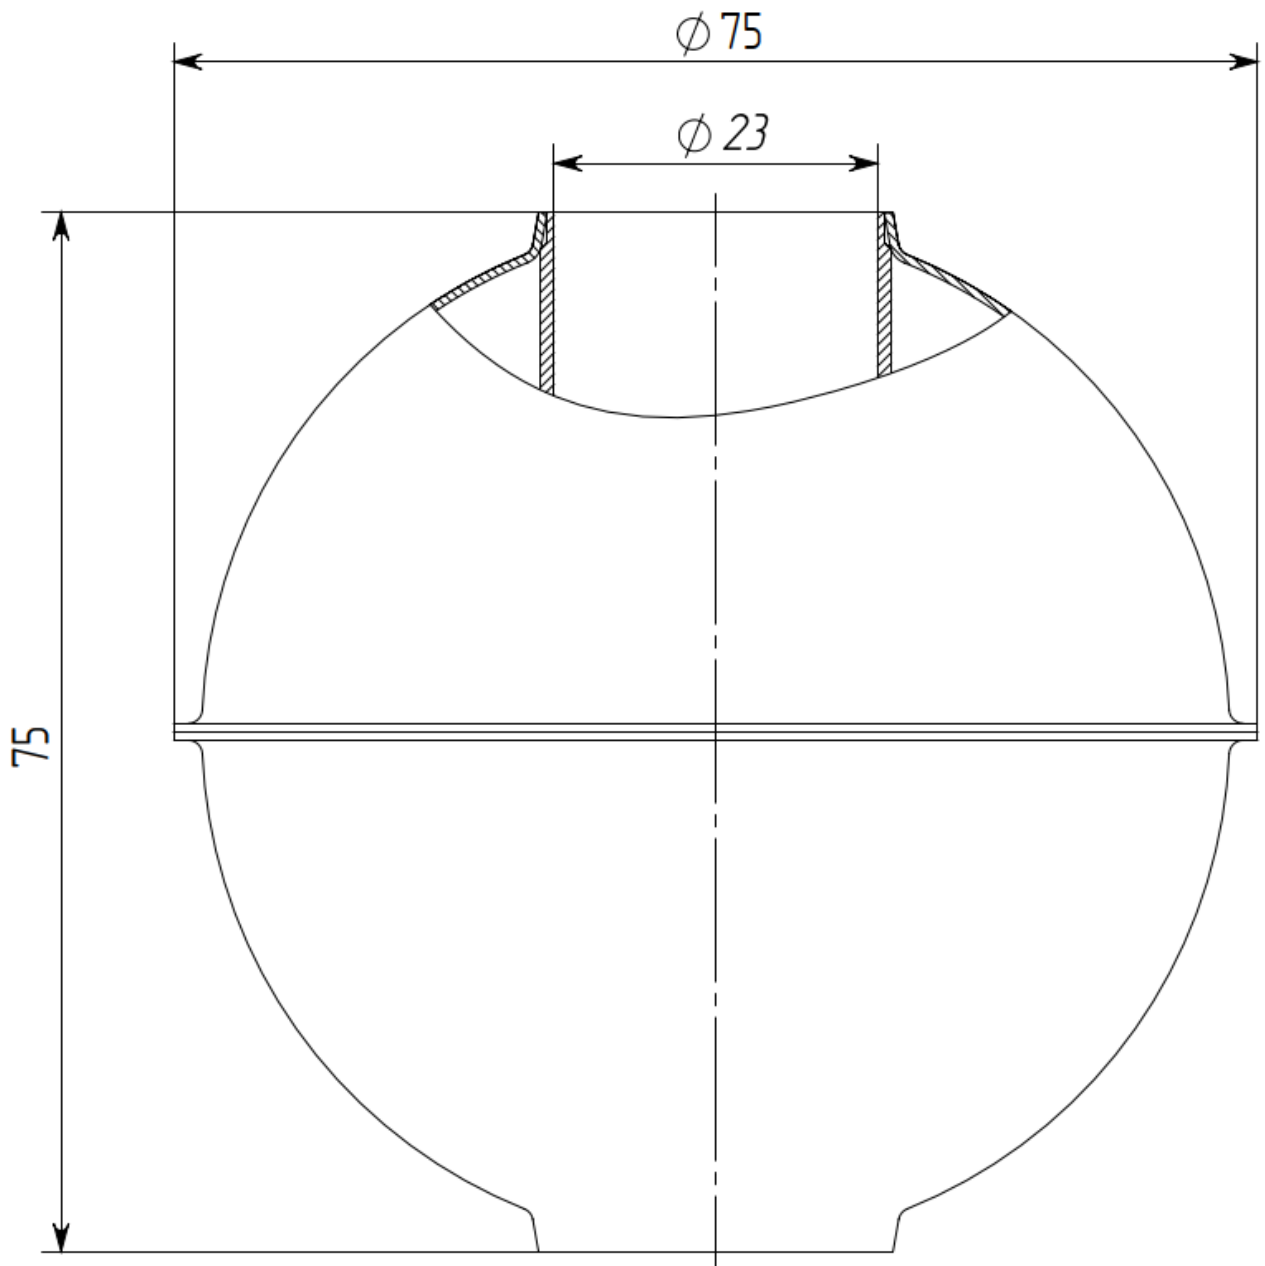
Габаритные и установочные размеры поплавка Н75 (масса 132 г) и Т75 (масса 72 г)
